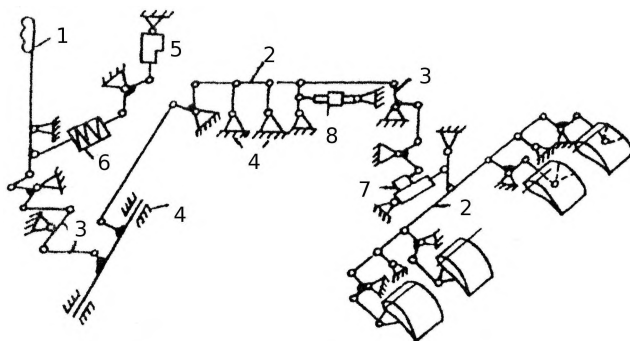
Схема канала крена системы управления: 1 — ручка управления; 2 — тяга; 3 — качалка; 4 — кронштейн; 5 — механизм триммерного эффекта; 6 — загрузочный механизм; 7 — бустер; 8 — рулевая машина автопилота
